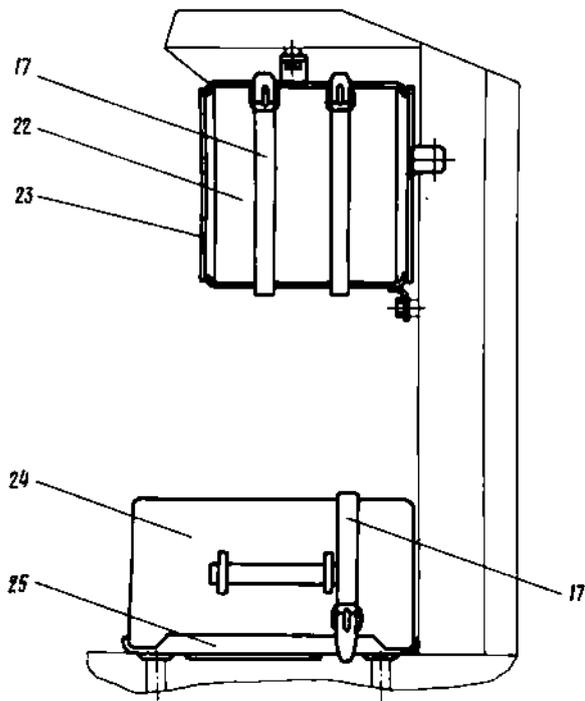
УКЛАДКА ЗИП В КОРПУСЕ 172.91.002с6-5
